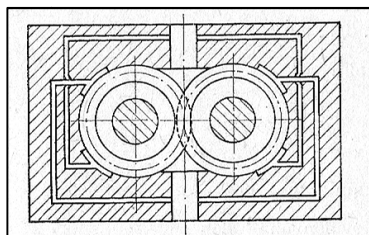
Uspořádání drážek uvolňujících škodlivý prostor S zubového čerpadla [1]
